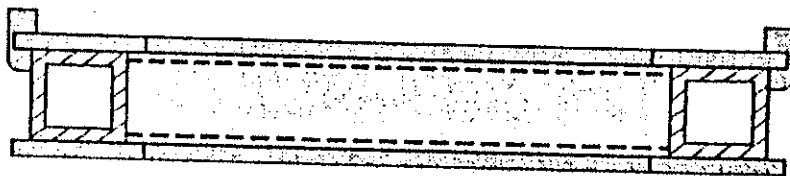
Контроль сварных швов внутренней поперечной балки рамы
